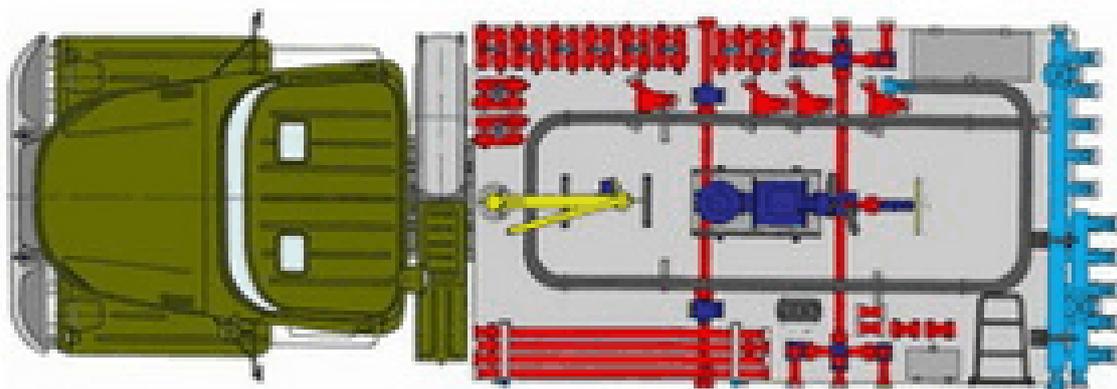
Общий вид блока манифольда (вид сверху)
